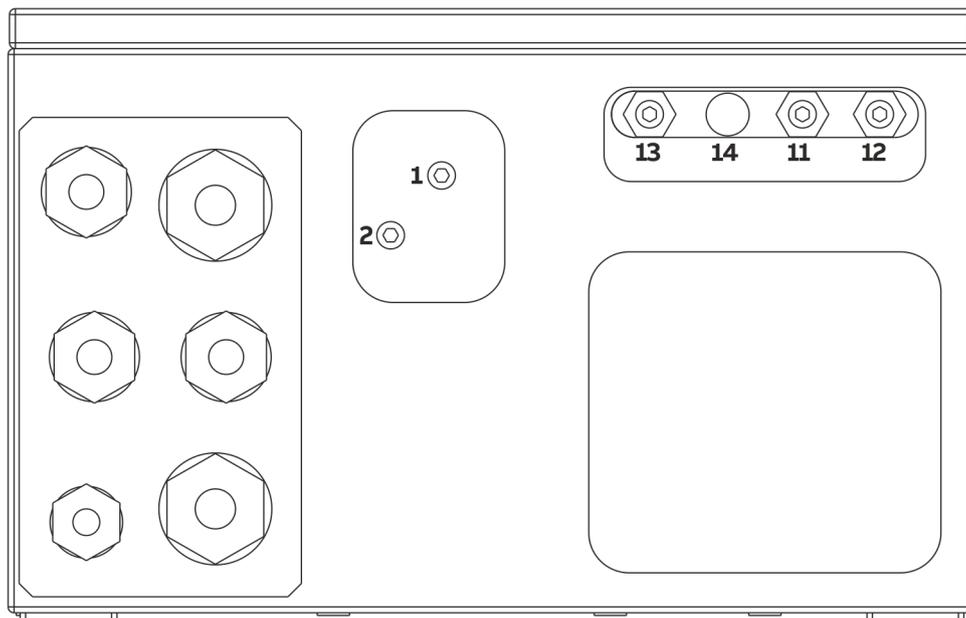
Gasanschlüsse Magnos28 (Modell EL3040)
